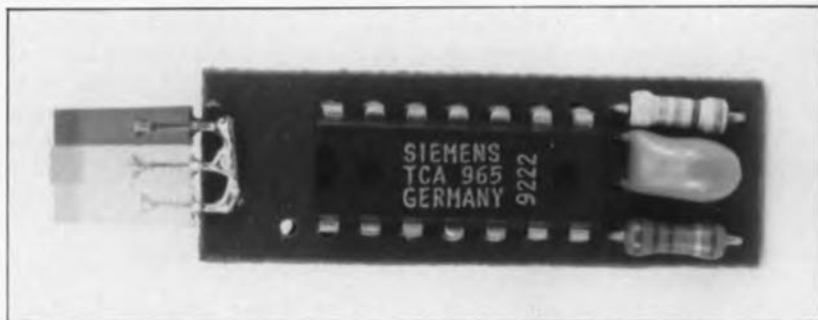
Vue du côté « composants » de la platine de notre prototype.
